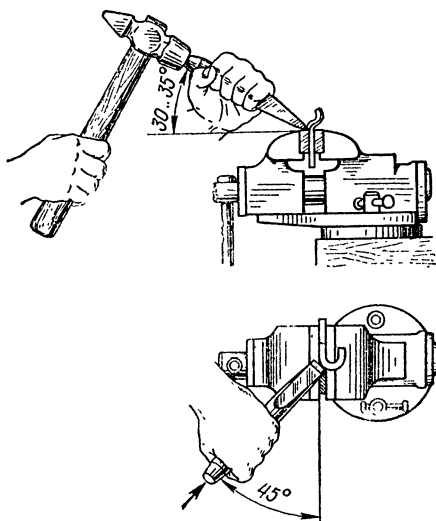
Положение зубила при рубке заготовки в тисках
